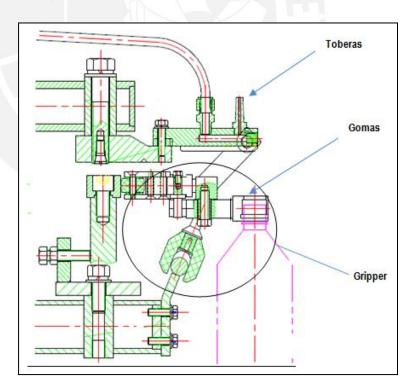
Máquinas del Tri-block Fuente: La Empresa
